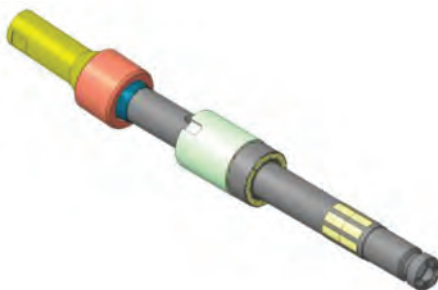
Конструкция шпинделя с радиальными опорами и шарнирным соединением
